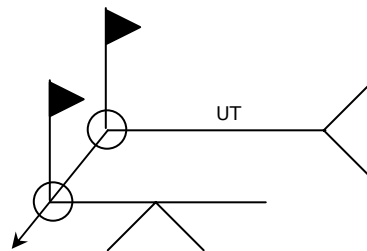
Símbolo de soldadura de campo para todo alrededor
